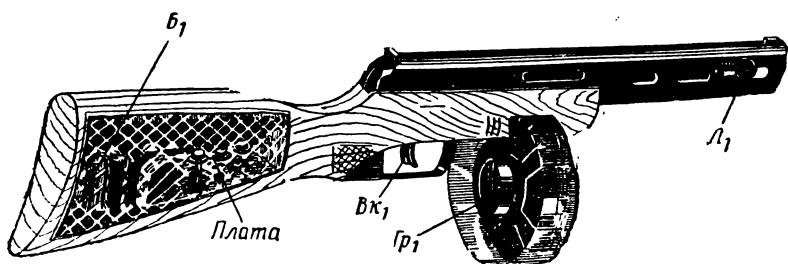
Размещение деталей в корпусе фоноавтомата.
